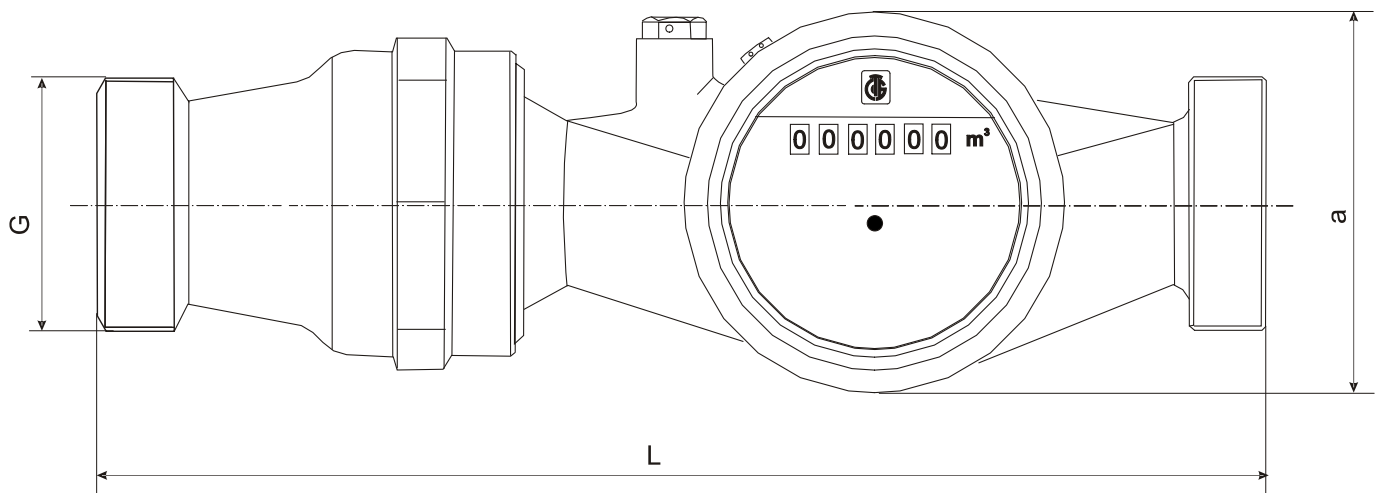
Габаритные и установочные размеры ППР крыльчатых DN 25, 32 и 40
